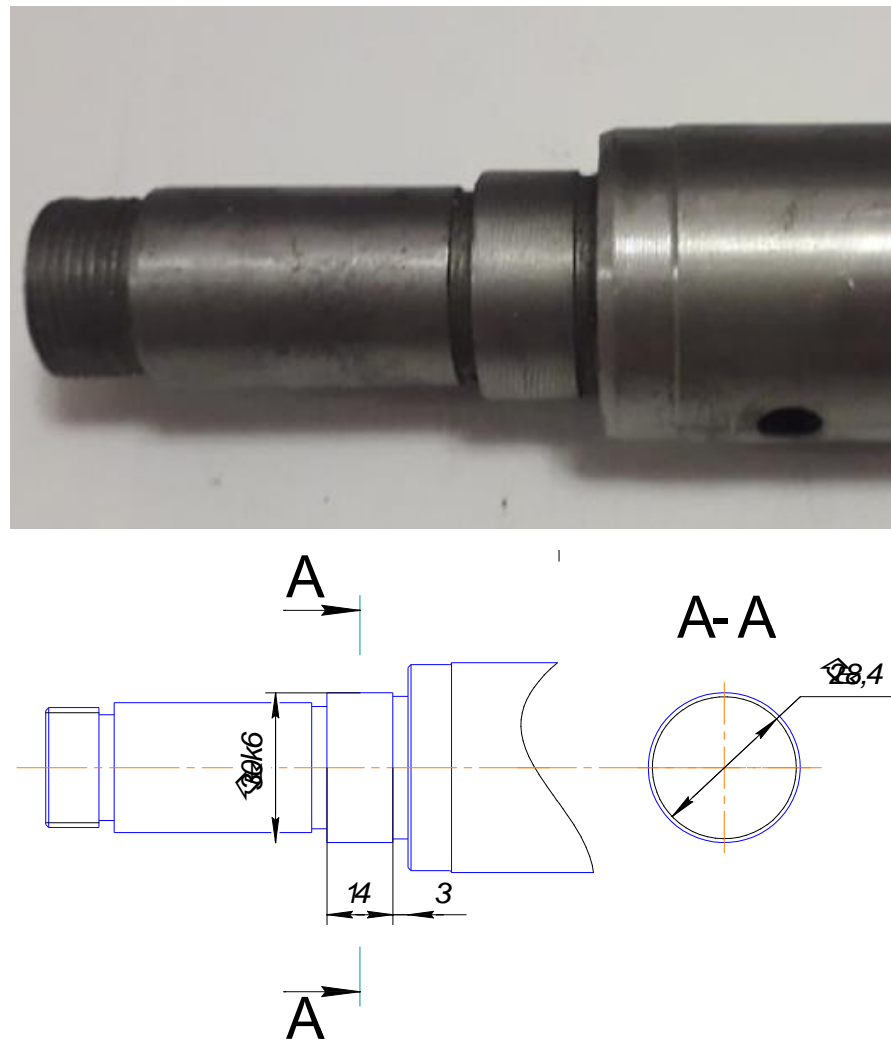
Поверхность 6 износ шейки вала – посадка под подшипники
